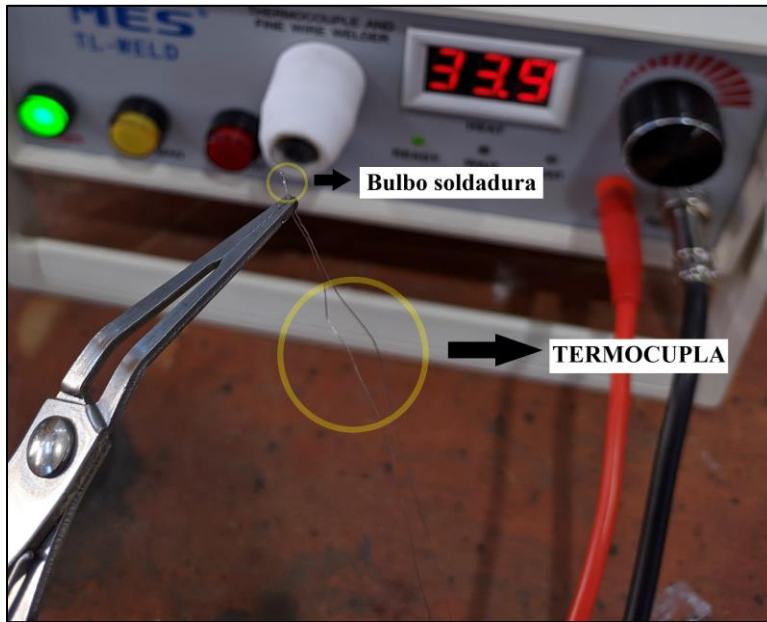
Termocupa tipo “S” unida por soldadura.
